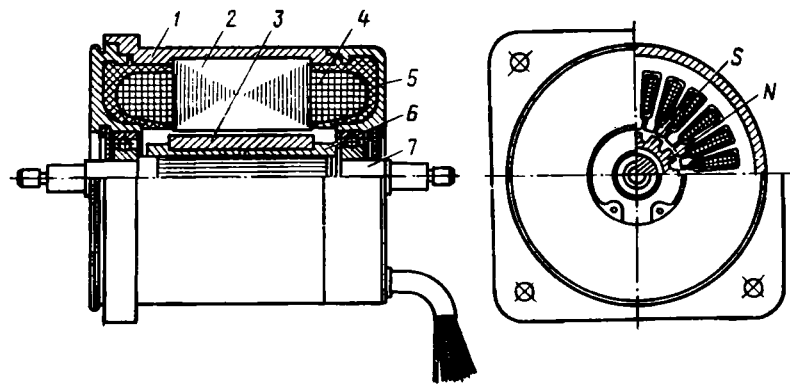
Шаговый исполнительный двигатель серии ШД:
